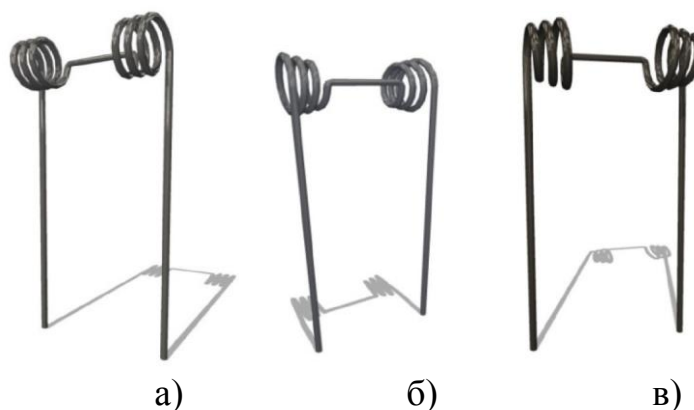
Пропоновані конструкції конусності пружиною частини зубопружинних робочих органів а) циліндрична (нульова); б) пряма; в) зворотна
